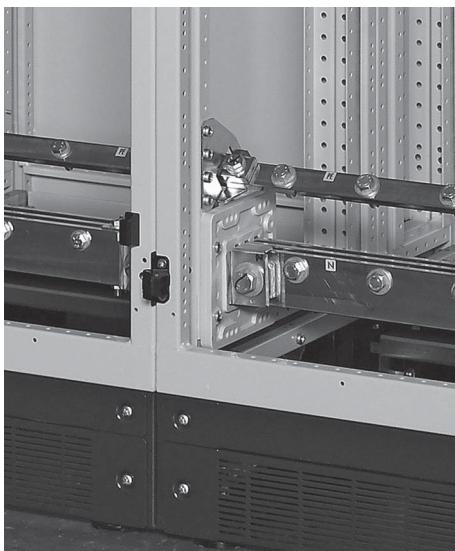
PE-Schiene direkt mit dem Schrankgerüst verbunden
